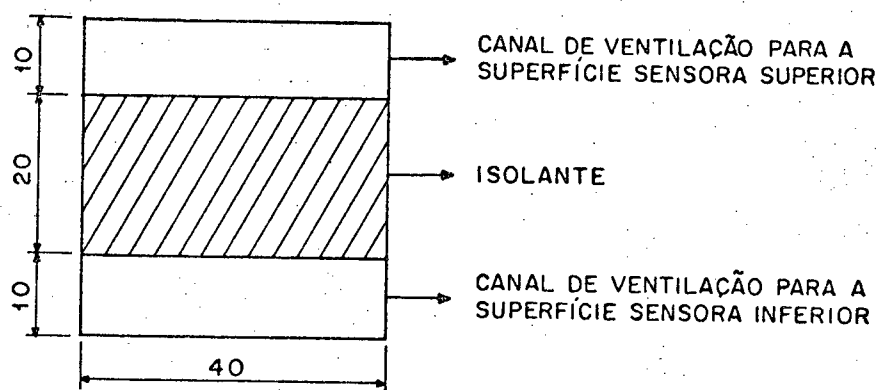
Dimensões das aberturas na parte final do duto de ventilação (em mm).
